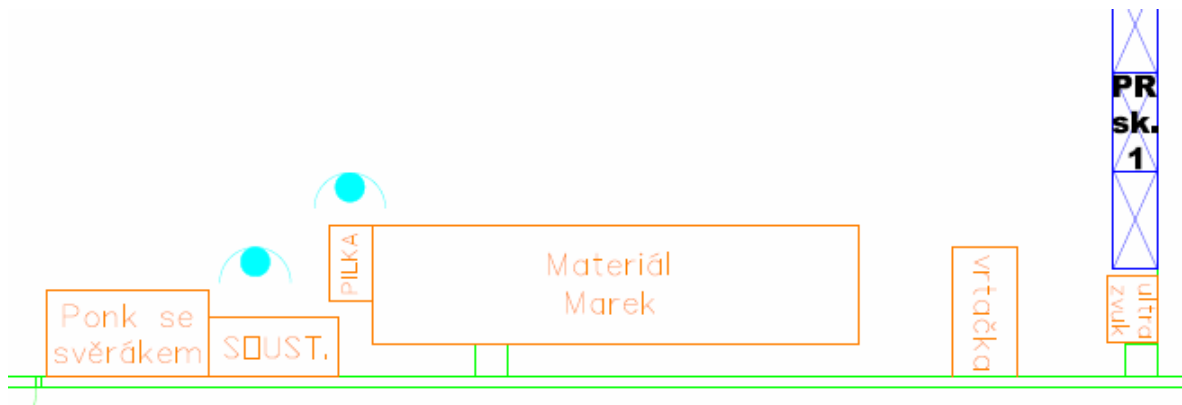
Layout pracoviště zdrojů (vlastní zpracování)
